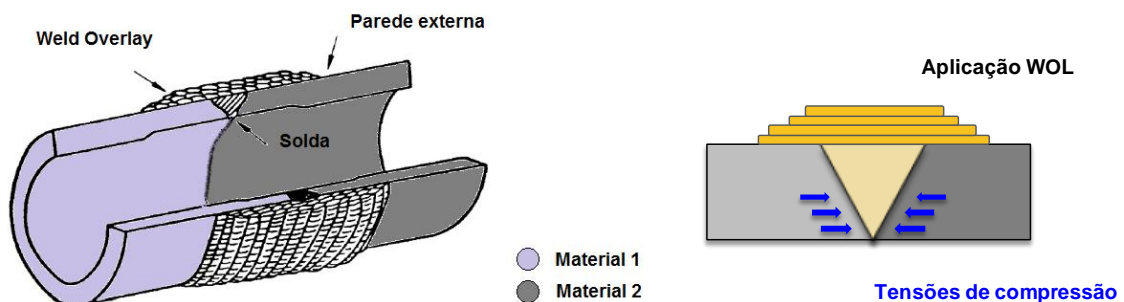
Aplicação da técnica *Weld Overlay* em juntas soldadas tubulares (EPRI - NP-7103-D, 1991).
